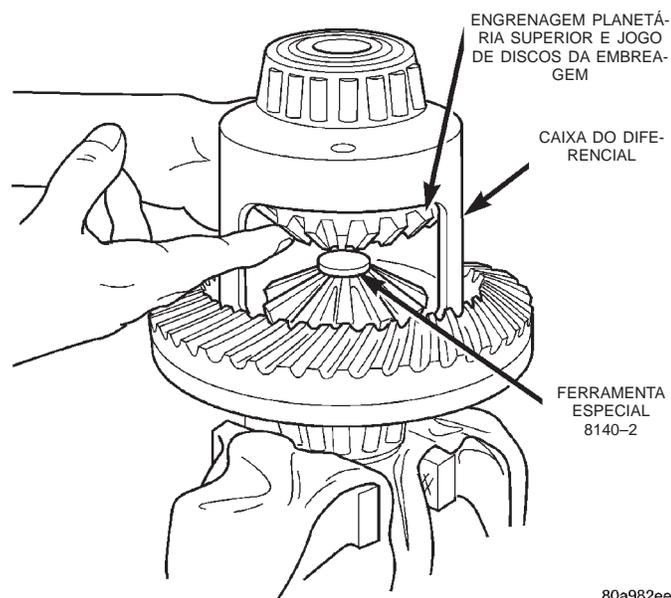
Engrenagem Planetária Superior e Instalação do Jogo de Discos da Embreagem
